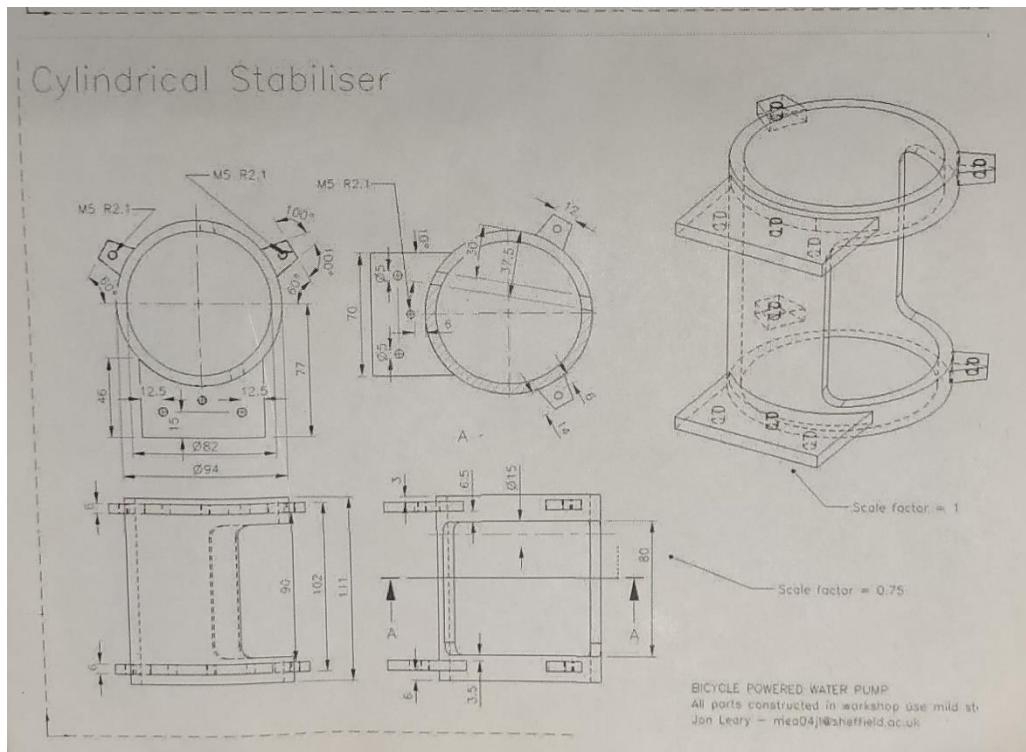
Plano de la pieza que ancla la bomba al rodillo.
